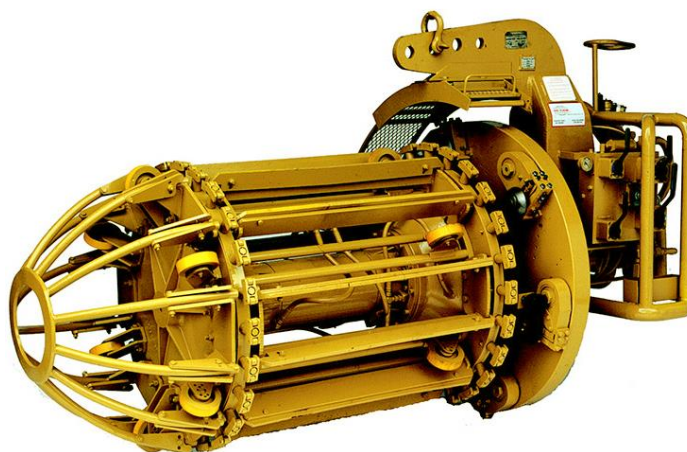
Станок для подготовки кромок труб PFM CRC-Evans
